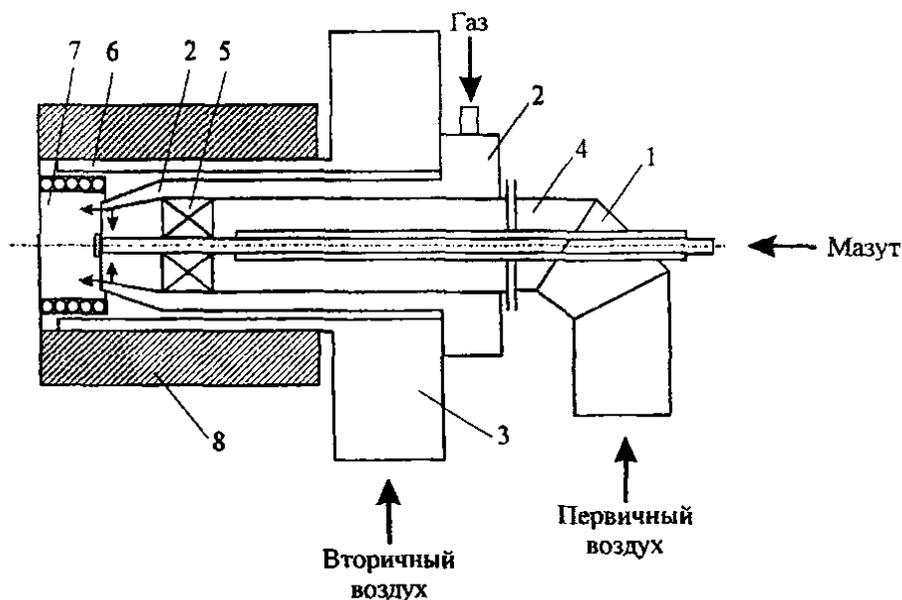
Схема газомазутной горелки для двухступенчатого сжигания топлива котла ДКВР-10-13.1-мазутная форсунка; 2-газовый коллектор; 3-улитка вторичного воздуха; 4-короб первичного воздуха; 5-аксиальный лопаточный завихритель; 6-катал вторичного воздуха; 7-газификационная камера; 8-обмуровка котла
